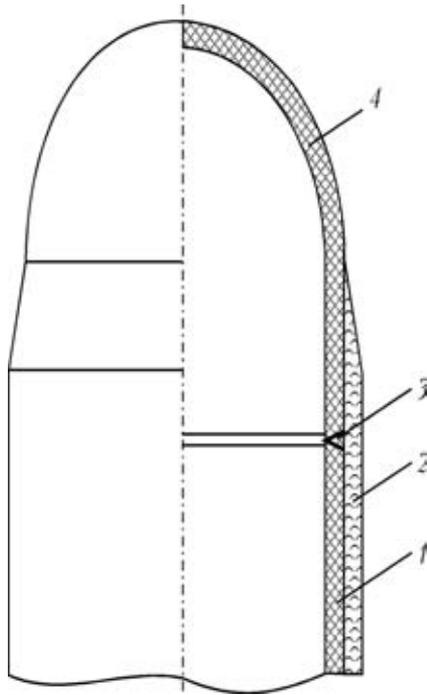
Схема комбинированного баллона со сварным корпусом из листовой стали: 1 — обечайка; 2 — оболочка; 3 — стыковое соединение; 4 — днище
